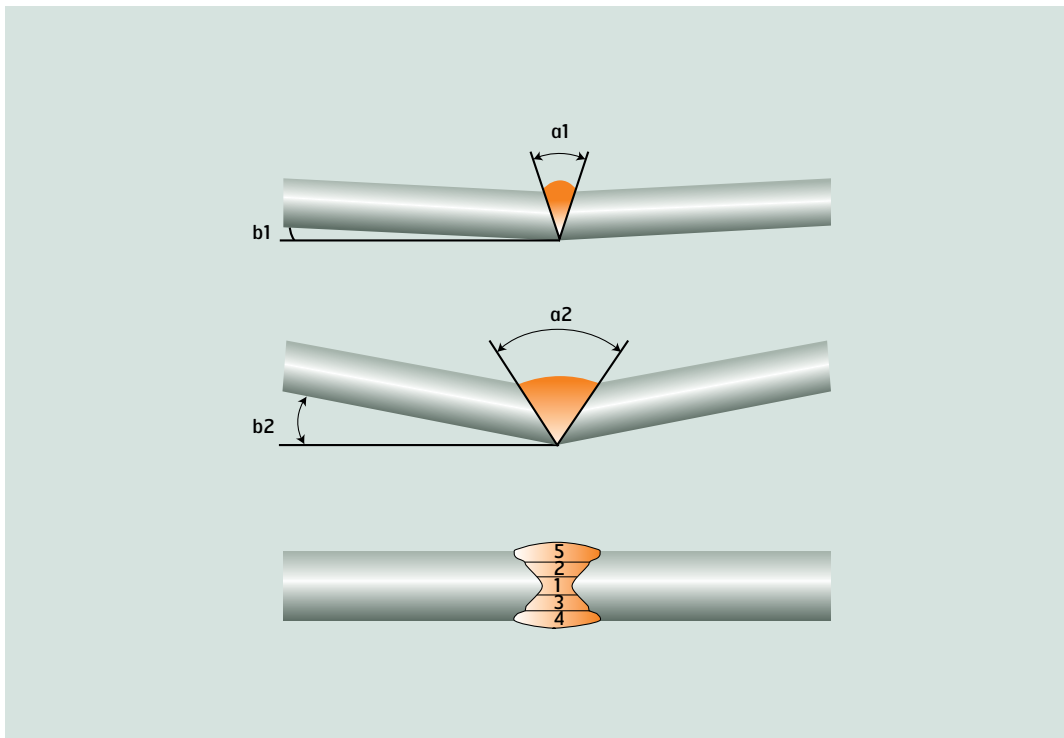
Предварительная установка для углового сварного соединения и стыкового соединения с односторонней разделкой кромок.
